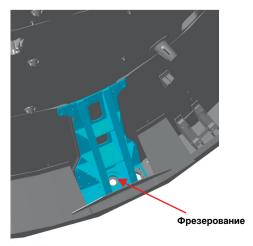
Элементы в склеенных заготовках, полученные фрезерованием
